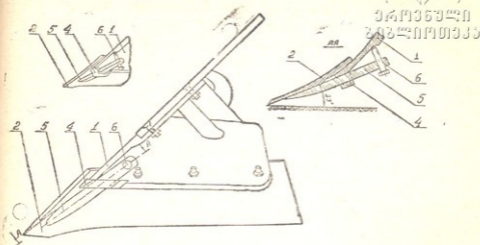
Плужный корпус: а — общий вид; б — разрез А-А; в — часть плужного корпуса, вид снизу.
